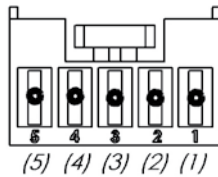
MOTORVERBINDUNG ANSICHT - SEITE DES KABELINGANGS
